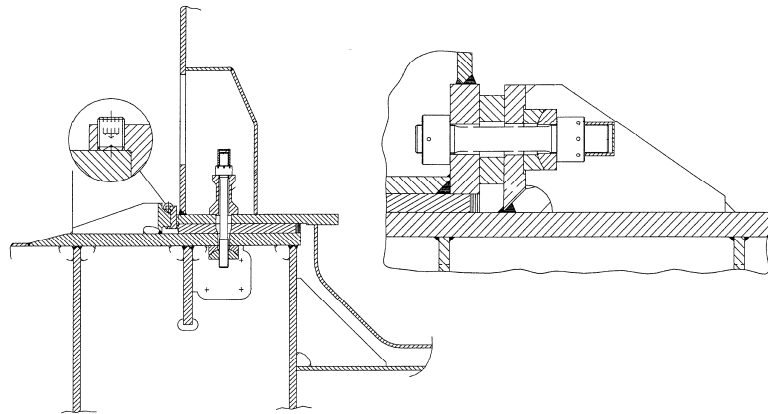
Кріплення фундаментної рами до фундаменту судна
